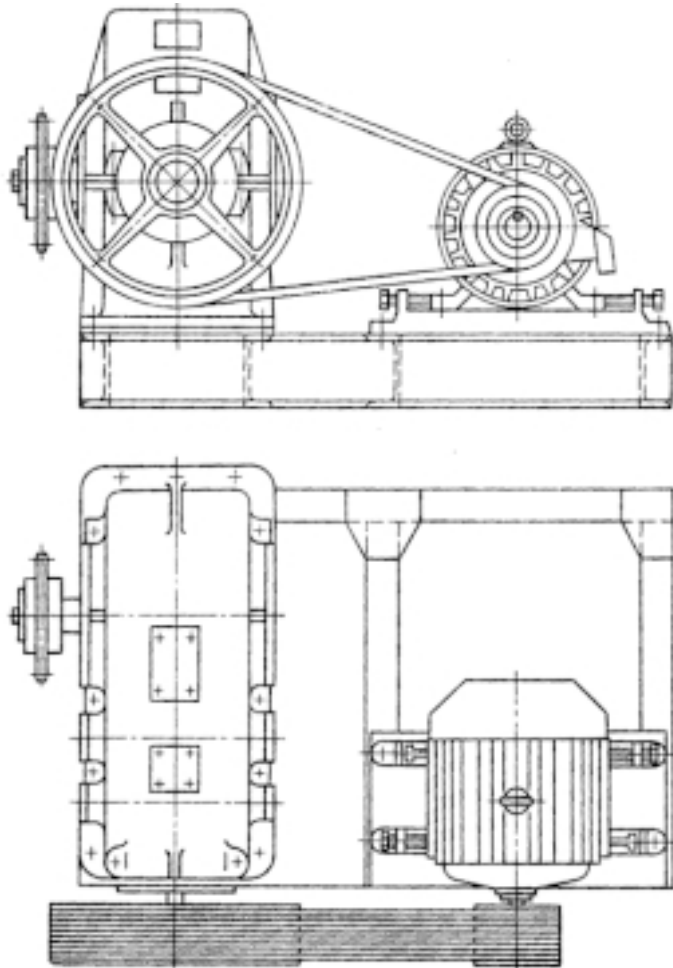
Общий вид привода с коническо-цилиндрическим редуктором
